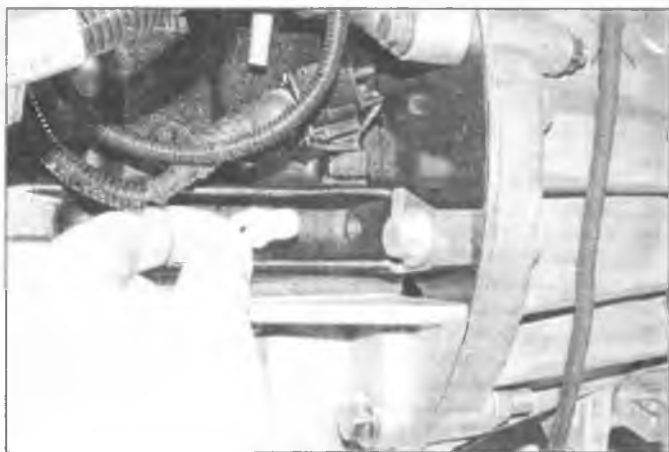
Извлеките заглушку из отверстия для установочного стержня в блоке цилиндров
